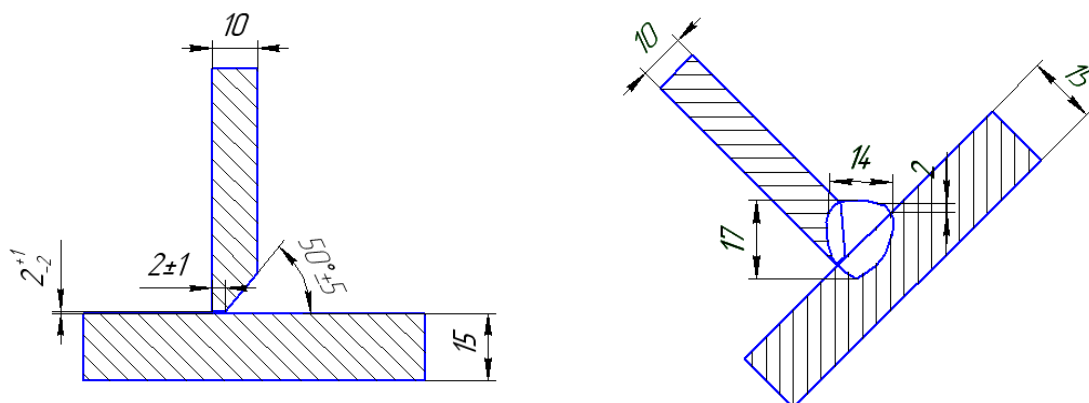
Эскиз сварного соединения Т7 по ГОСТ 8713-79
